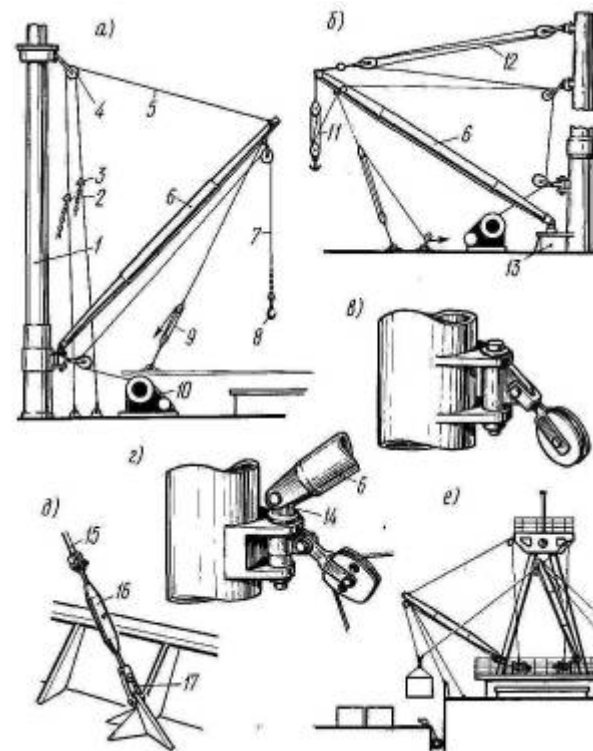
Грузовое устройство: а — легкая стрела; б — стрела-тяжеловес; в — д — элементы грузового устройства; в — башмак топенанта с блоком; г — крепление шпора грузовой стрелы; д — крепление вант к палубе; е — работа грузового устройства с двумя неподвижными грузовыми стрелами. 1 — мачта; 2 — цепочка топенанта; 3 — треугольное соединительное звено; 4 — топенантный блок; 5 — топенант; 6 — грузовая стрела; 7 — шкентель; 8 — гак; 9 — оттяжки; 10 — грузовая лебедка; 11 — грузовые тали; 12 — топенантные тали; 13 — фундамент грузовой стрелы; 14 — вертлюг; 15 — концевая обойма; 16 — талреп; 17 — скоба.
